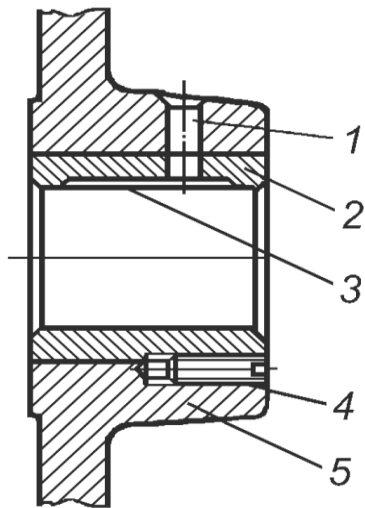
Неразъемный подшипник скольжения, встроенный в станину машины:
